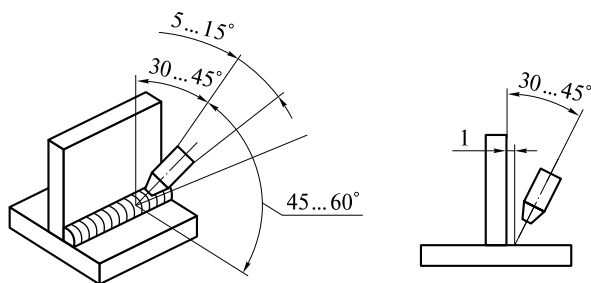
Положение горелки при сварке угловых швов
